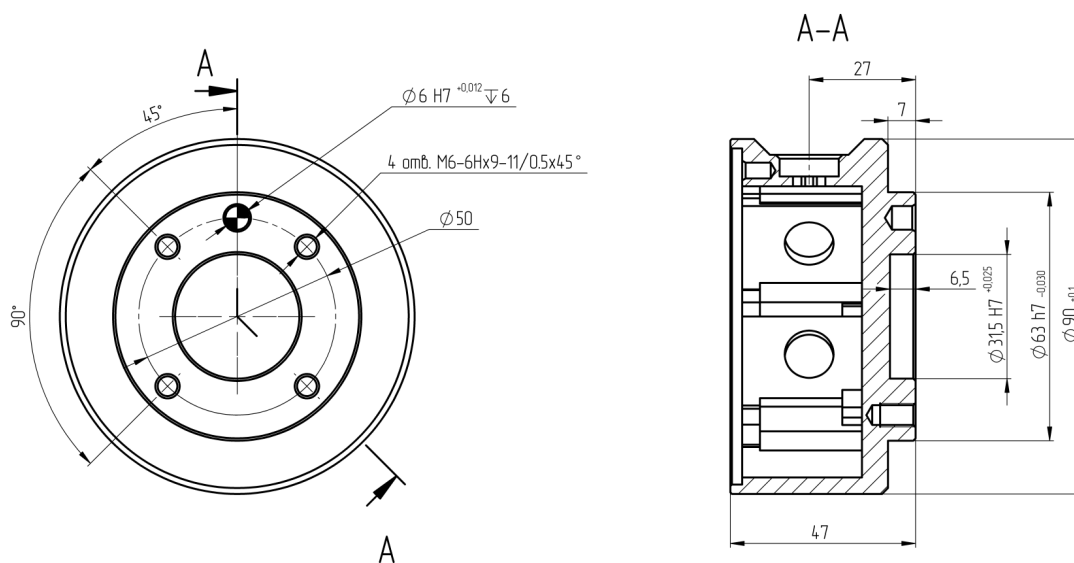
Габариты фланца для подсоединения инструмента и схема расположения отверстий
